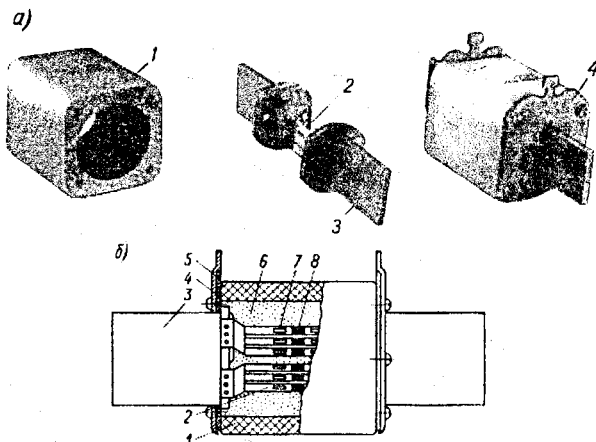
Запобіжники серії ПН-2: а) загальний вигляд і деталі б) розріз
